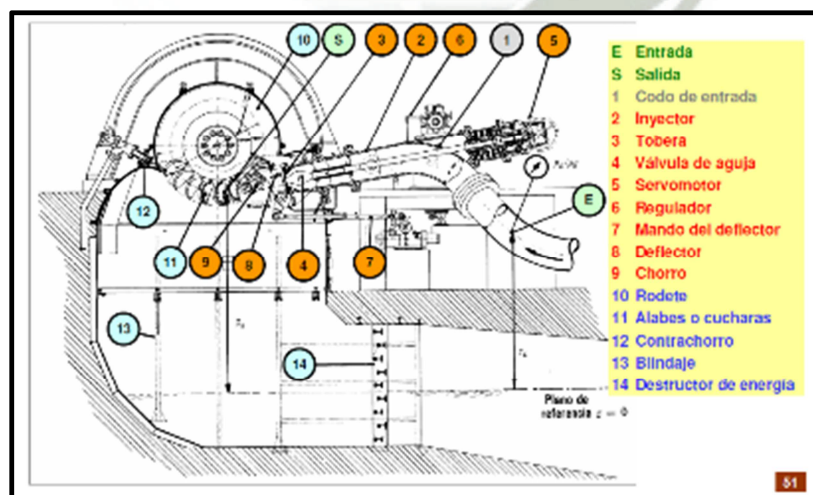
Componentes de una Turbina Pelton de Eje Horizontal
